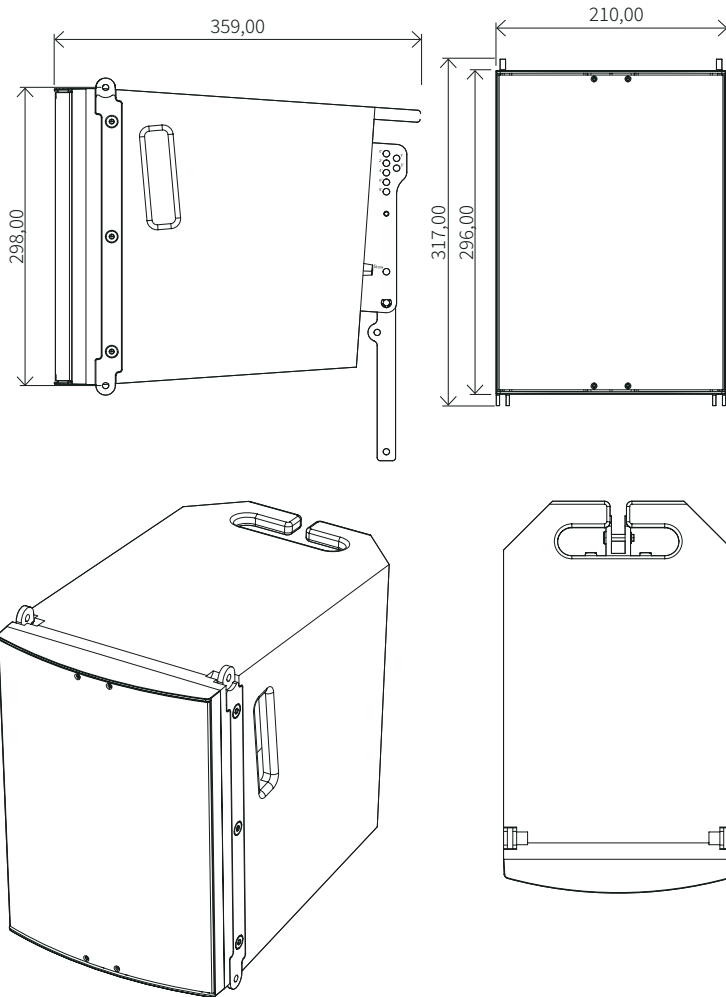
M-F3A PRO Ansichten und Abmessungen. Bemaßung in Millimetern
